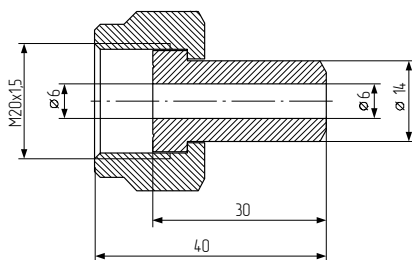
Габаритные размеры приварного ниппеля
